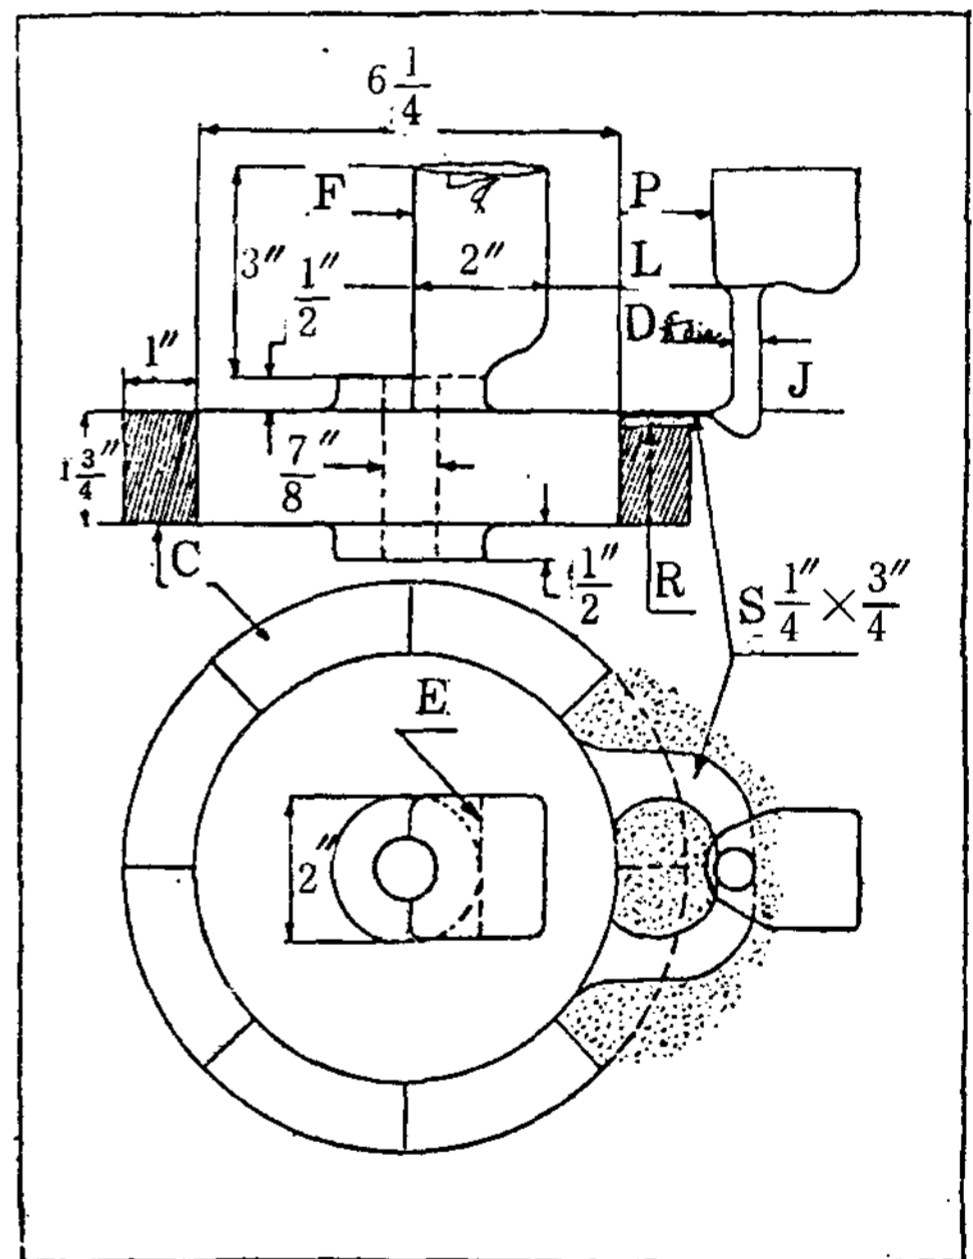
인칭동 gear blank 를 제조하기 위한 주조 방안.
